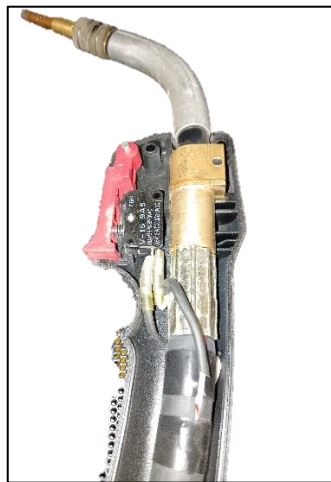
Antorcha de soldadura MIG
